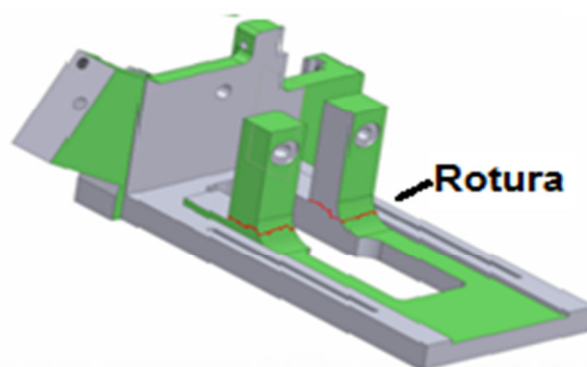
Carro contra-compressor das maquinas AMF e zona de ruptura
